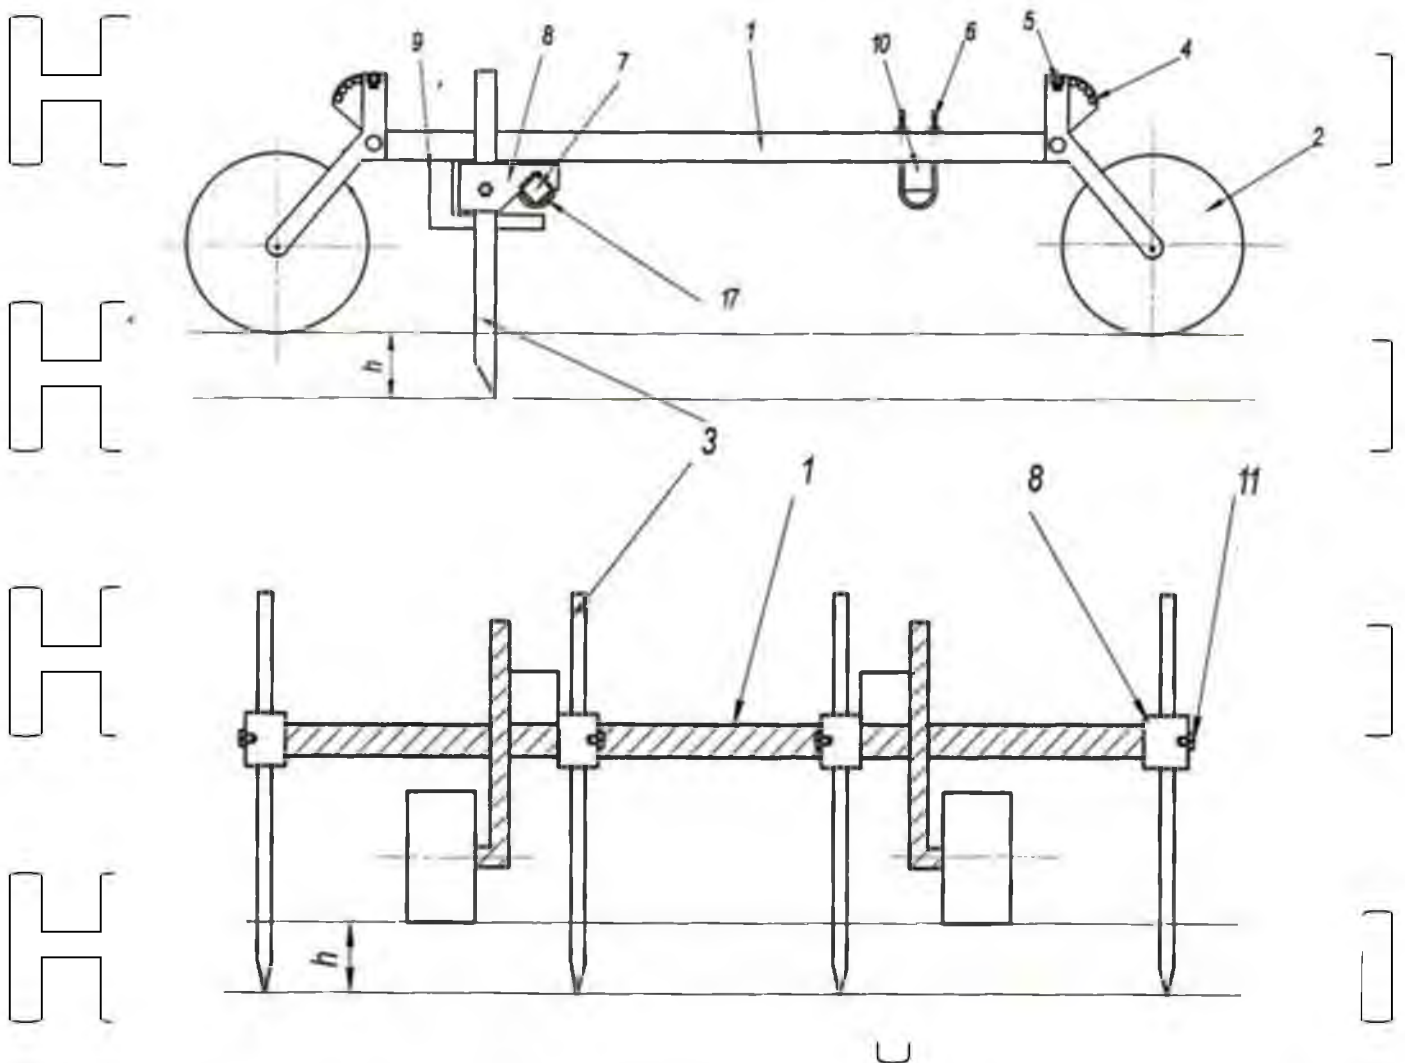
Загальний вигляд макетної лабораторно-польової установки (вид збоку і ззаду): 1-рама; 2- колеса; 3- електроди; 4-регулювальний сектор; 5- болт регулювального сектора; 6-голівки; 7-градус; 8- крошітей; 9- обмежувальна смуга; 10-поперечна балка; 11-кріплення електродів; 17- ізолюючий матеріал.
